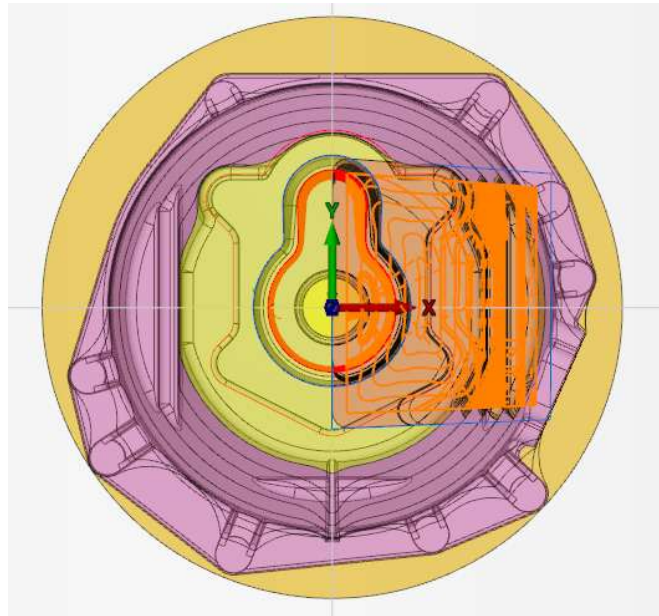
Usinage 3D limité par une frontière (Séquence – représenté par un trait bleu)
